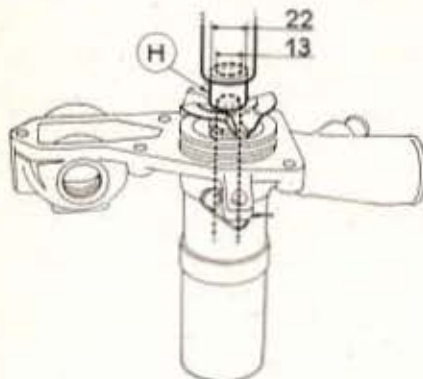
Mise en place, sous presse, de l'ensemble joint-turbine
